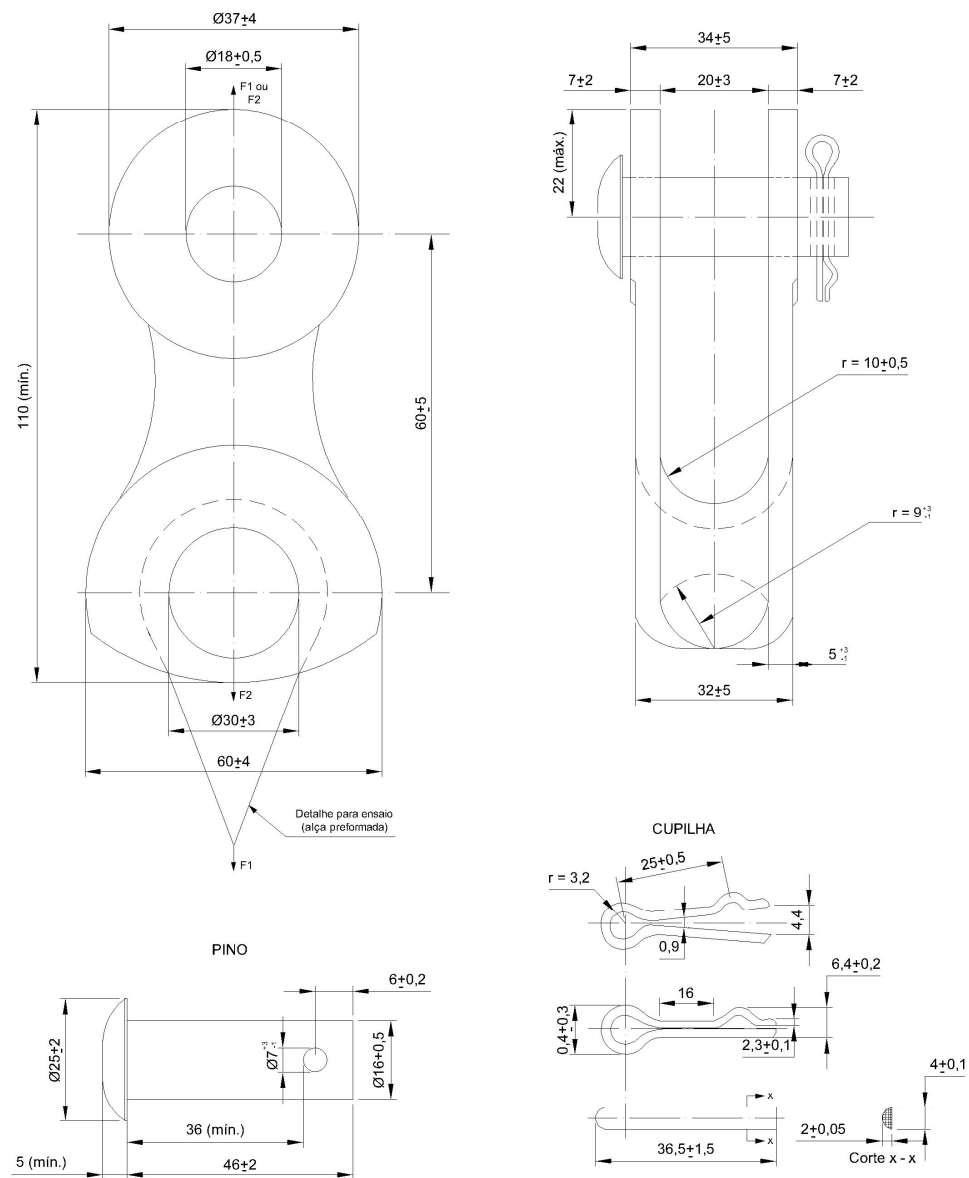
Desenho dimensional conjunto manilha-sapatilha
